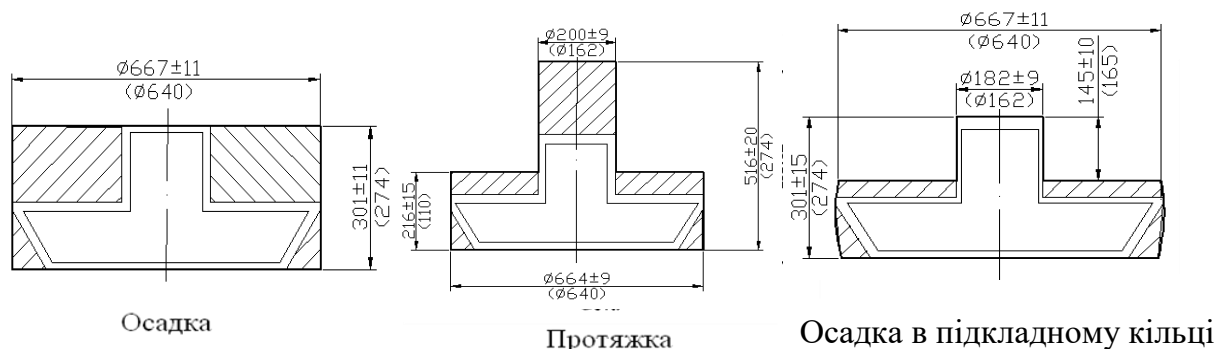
Креслення заготовок, що одержані існуючими способами штампування
